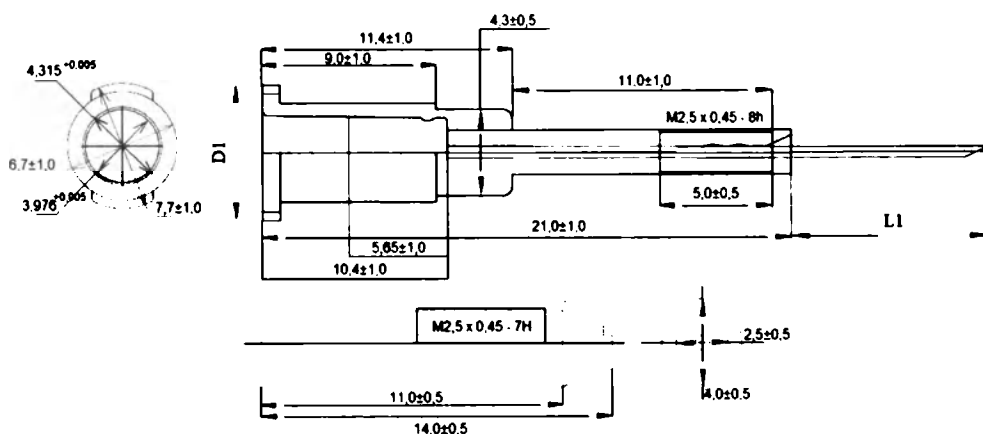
Размеры головки иглы Johns Screw Needle и «Луер» соединения по ISO 80369-7, присоединительный конус иглы по ISO 594-1.
